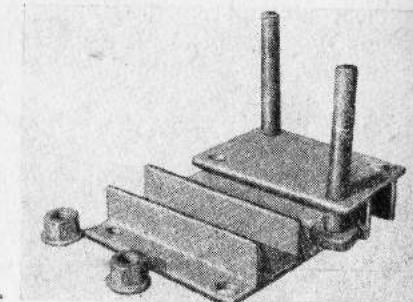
Приспособление для запрессовки брусьев кильсона.
